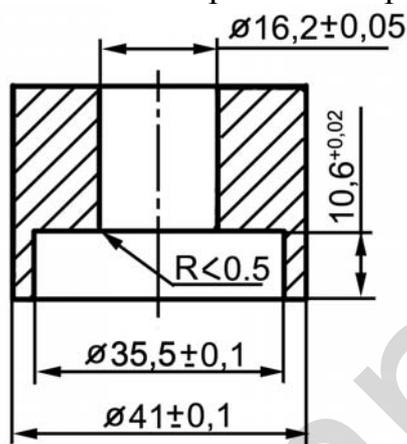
Оправка для запрессовки уплотнения водяного насоса (Основные конструктивные размеры)
